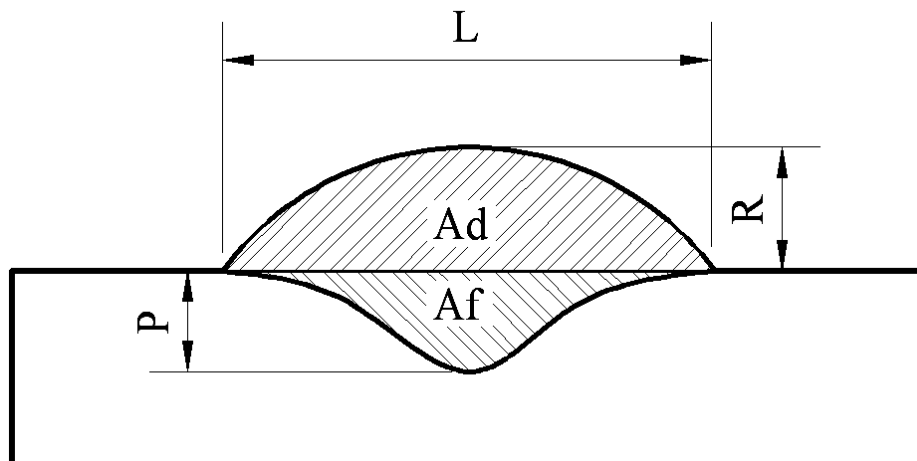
Representação esquemática das dimensões geométricas das seções transversais dos cordões de solda.
